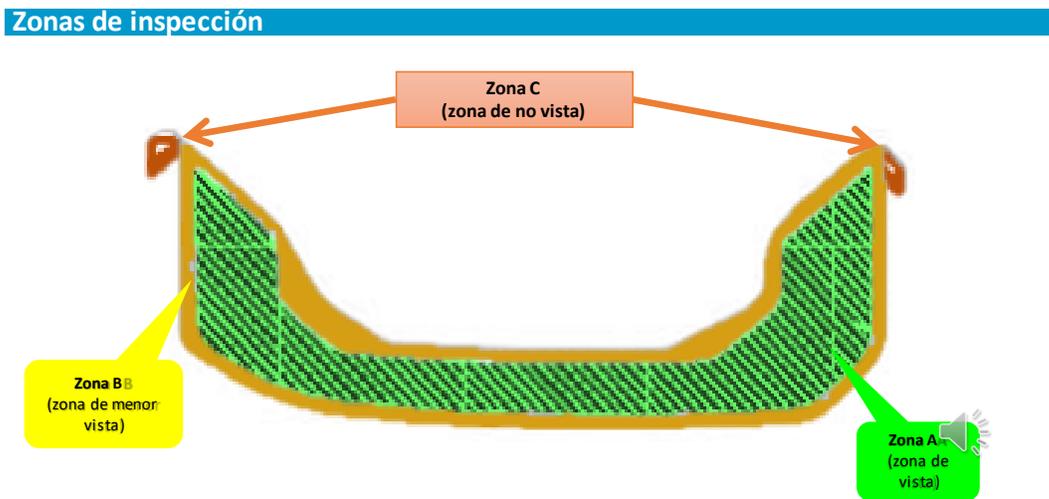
Zonas de inspección de la pieza Rear Side RR.
